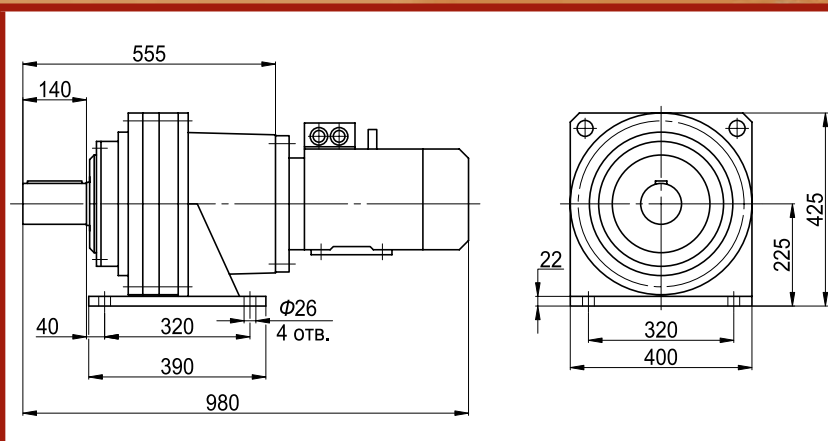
Общий вид и габаритно-присоединительные размеры привода
